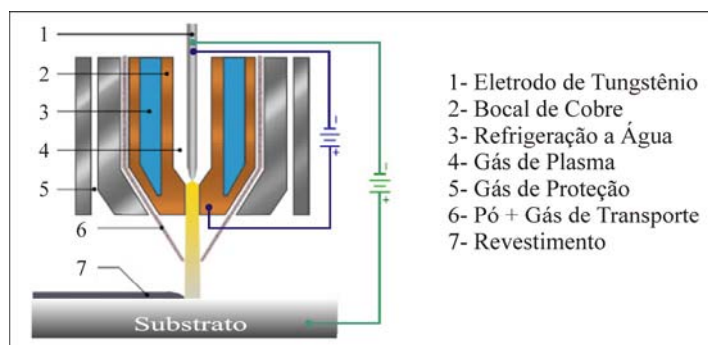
Desenho esquemático de uma tocha do PTA (adaptado de PTA and Weld Hardfacing).
